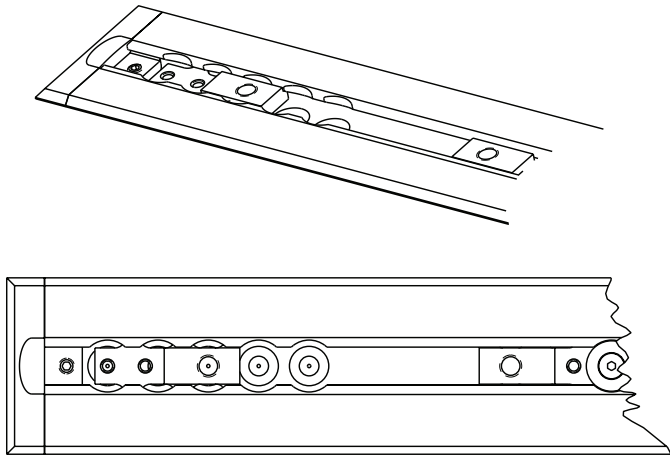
Inserire la staffa di fissaggio per la piastra a pavimento
